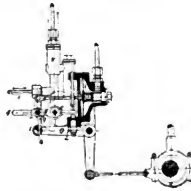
Deutzer Brennstoffpumpe mit Membransteuerung.
